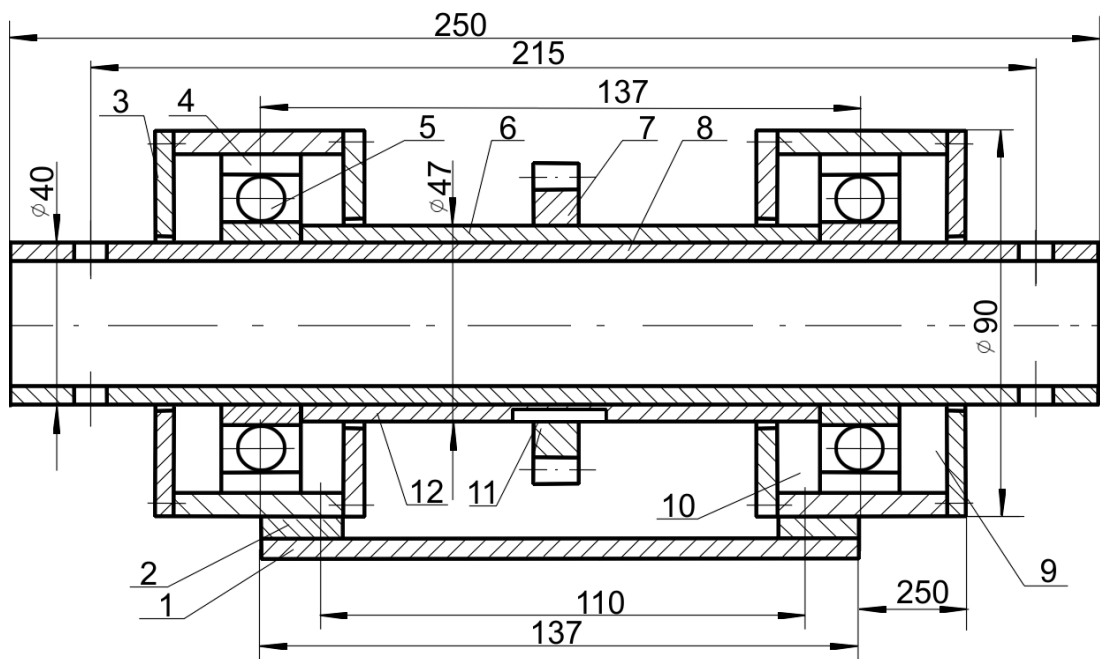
Схема крепления рабочих спиралей правой и левой навивки одной звездочкой: 1 – рама; 2 – опора; 3 – крыша; 4 – корпус; 5 – подшипник; 6 – втулка; 7 – звездочка; 8 – втулка; 9,10 – сальник; 11 – шпонка; 12 – вал
